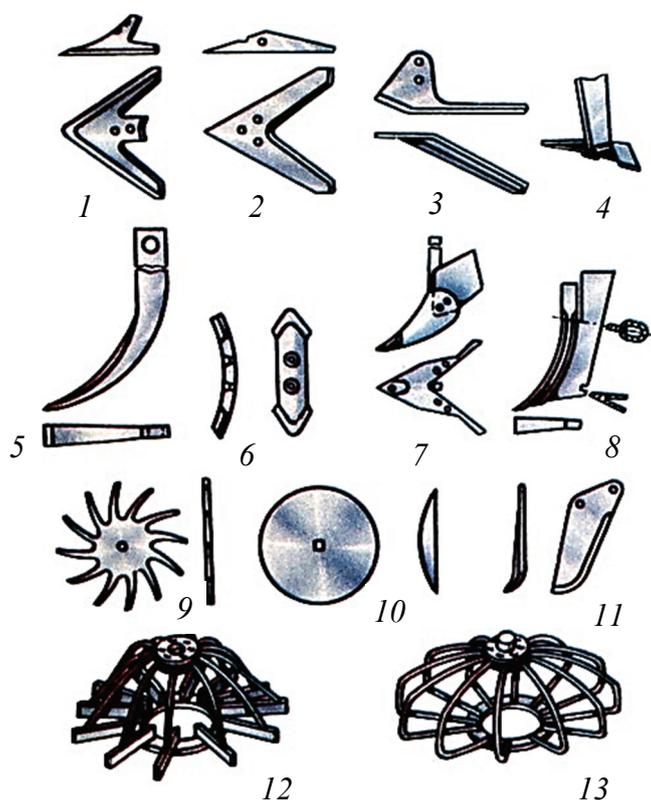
Рабочие органы культиваторов: 1 – универсальная лапа; 2 – стрельчатая двусторонняя лапа; 3 – то же, односторонняя; 4 – плоскорежущая лапа; 5 – долотообразная лапа; 6 – оборотная лапа; 7 – окучивающий и бороздорежущий корпуса; 8 – подкормочный нож; 9 – игольчатый диск; 10 – сферический гладкий диск; 11 – Г-образный нож; 12 – лопастная крыльчатка; 13 – проволочная крыльчатка
